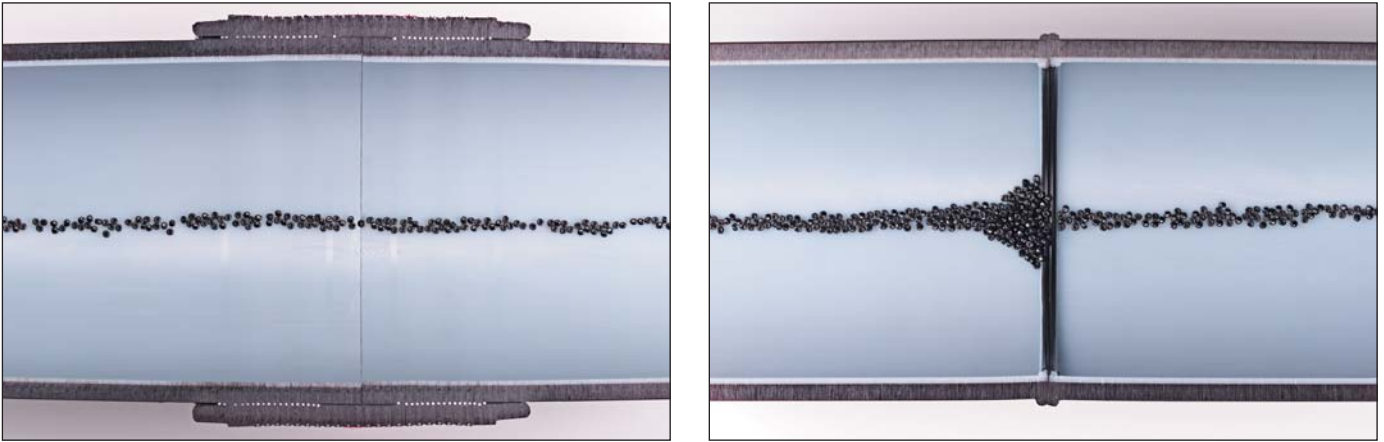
Vergleich einer Heizwendelschweißung (links) und einer Stumpfschweißung (rechts)
